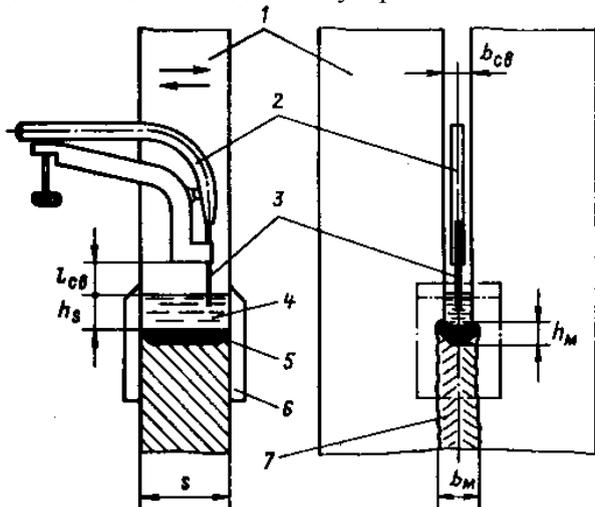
Схема электрошлаковой сварки:
